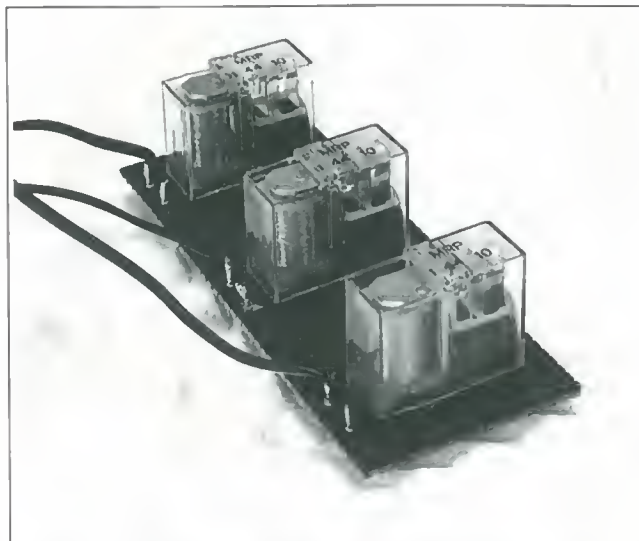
Il gruppo dei relé è stato assemblato su di una basetta millefori.
